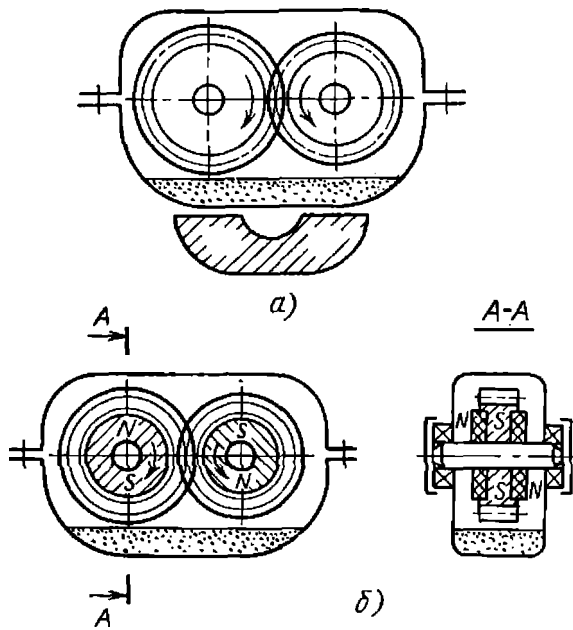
Магнитопорошковый метод смазывания зубчатых колес:
